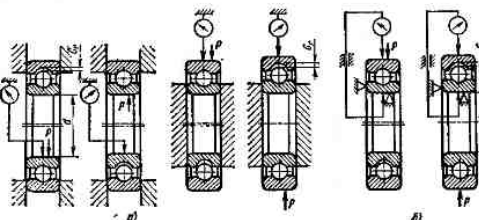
Схема измерения радиального зазора: а — с креплением колец по торцу; б — без крепления колец; G_r — радиальный зазор; P — измерительная нагрузка
